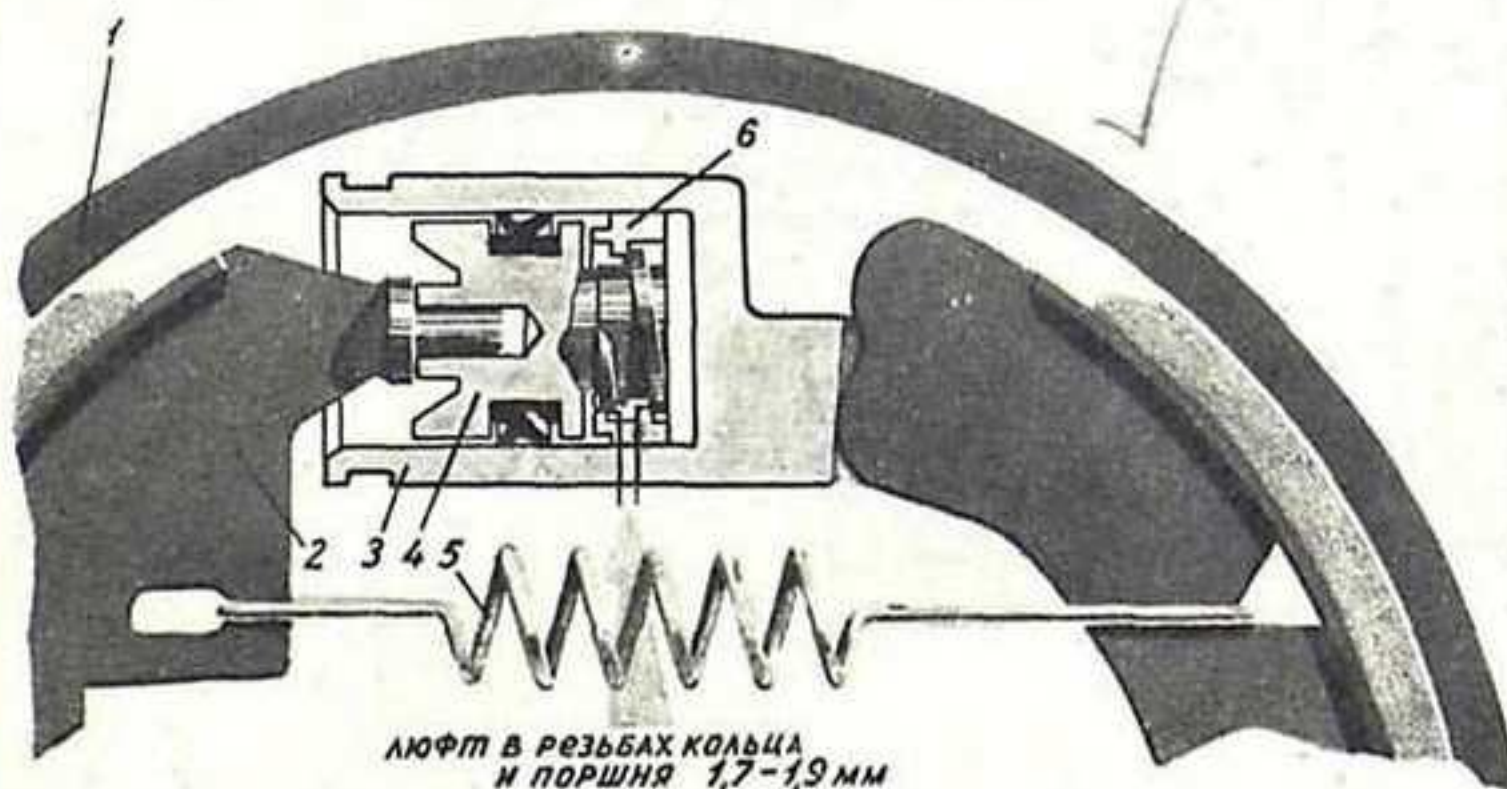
Схема автоматического устройства для поддержания зазора между колодкой и барабаном: 1 — барабан; 2 — колодка; 3 — колесный цилиндр; 4 — поршень; 5 — стяжная пружина; 6 — разрезное пружинное кольцо.
